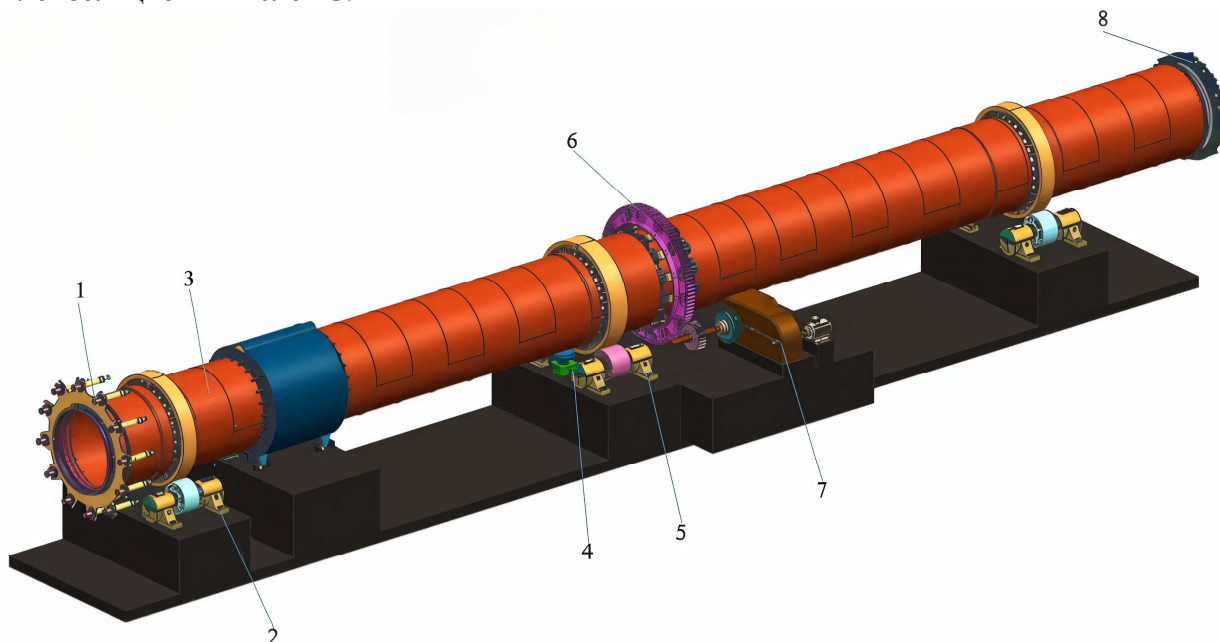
Цифровой двойник вращающейся печи: 1 – уплотнение горячего конца; 2 – роликоопора; 3 – корпус; 4 – ролик упорный; 5 – роликоопора; 6 – открытая зубчатая передача; 7 – привод; 8 – уплотнение холодного конца печи; 9 – теплообменное устройство
